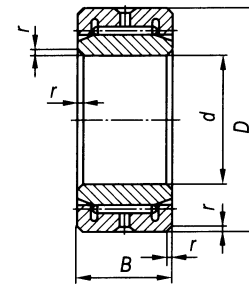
Подшипник роликовый радиальный иглочатый однорядный
